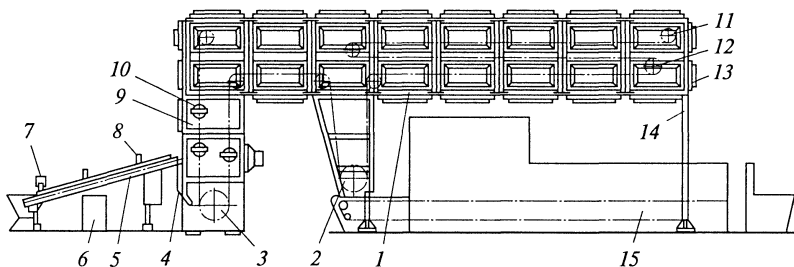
Шкаф Т1-ХРЗ для расстойки заготовок круглого подового хлеба
